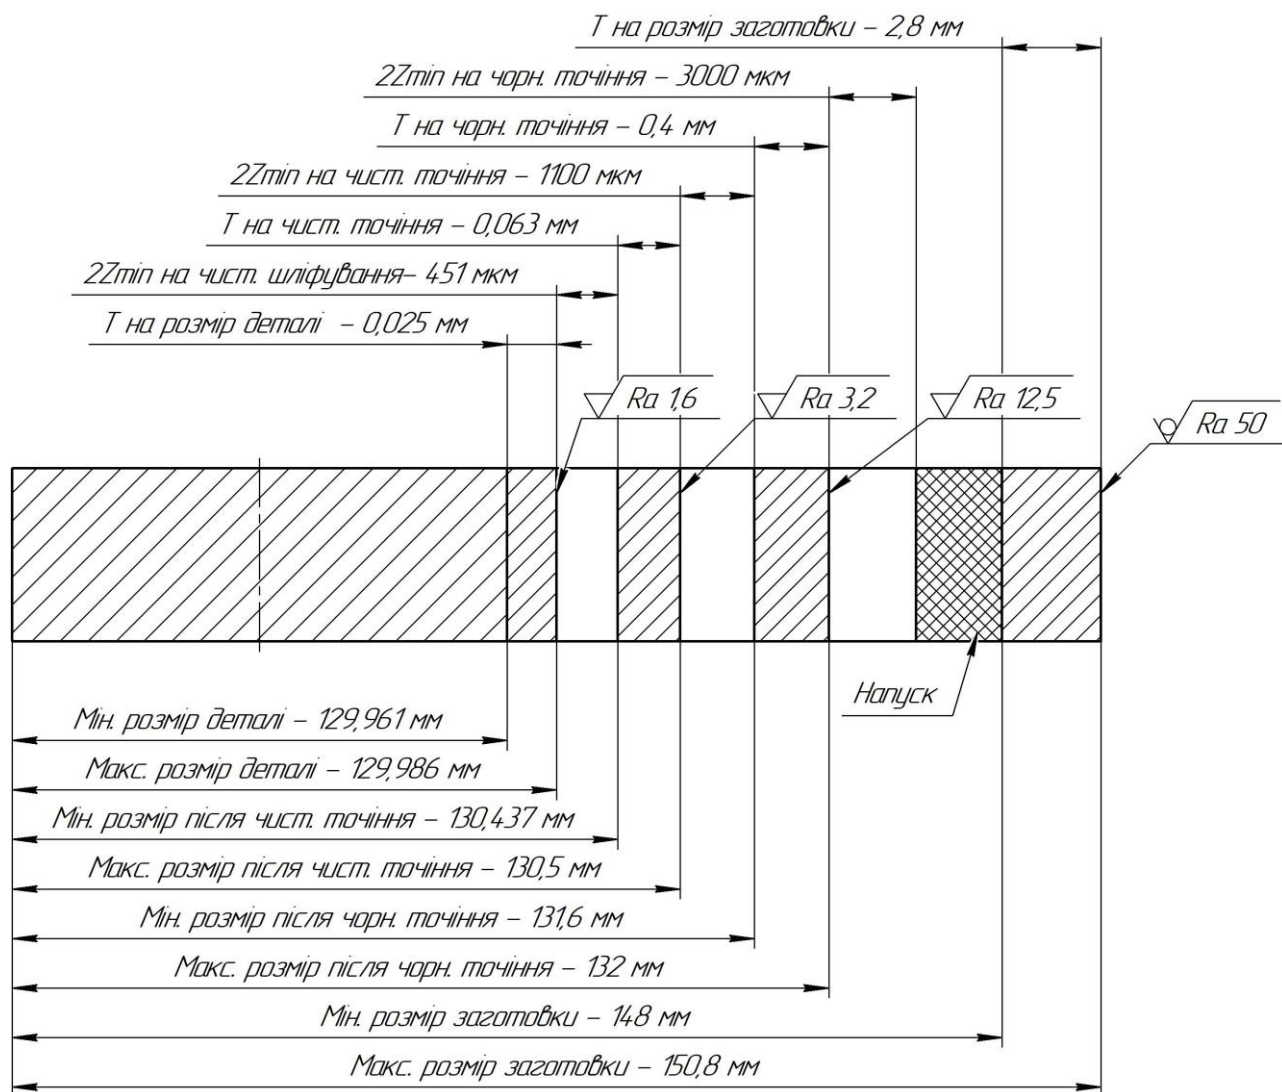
Схема розміщення полів припусків і допусків під час оброблення зовнішньої циліндричної поверхні $d130g6$
